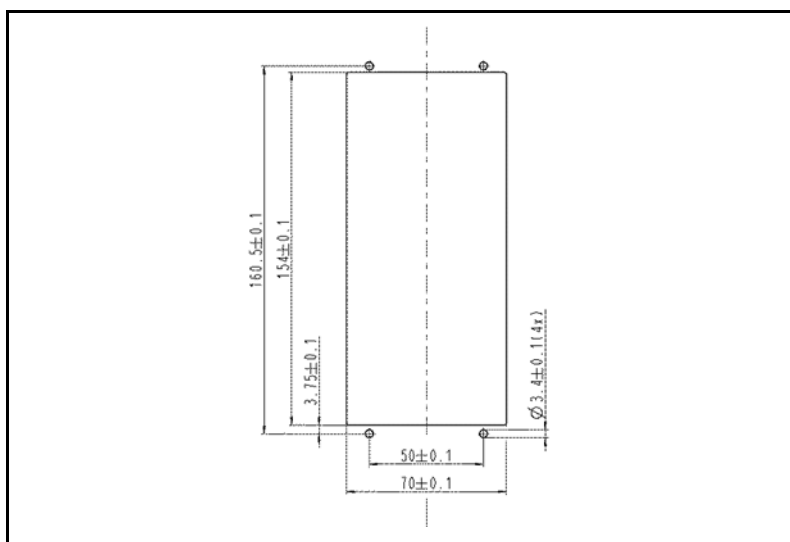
Dimensions pour le montage du contrôleur de vide
